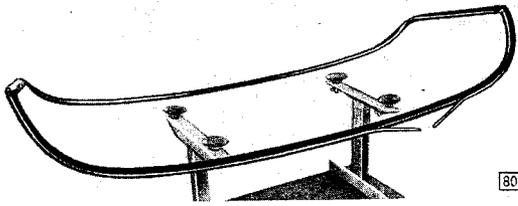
Gummischnur als Montagehilfsmittel in Gummifassung eingelegt – Windschutzscheibe
